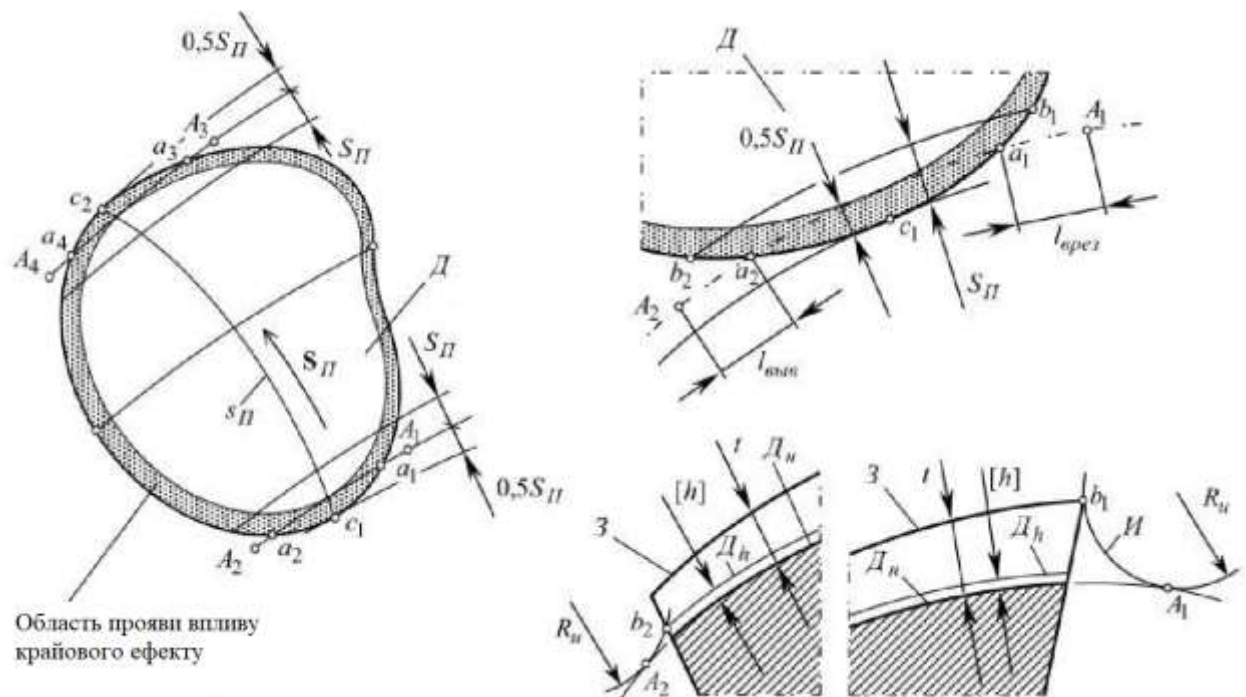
Визначення положення точки початку обробки складної поверхні деталі на багатокординатному верстаті з ЧПК [65, с. 502]
